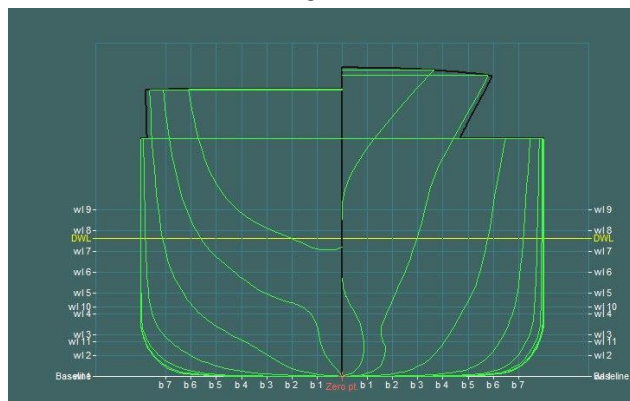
Створена 3D модель теоретичної поверхні корпусу балкера
